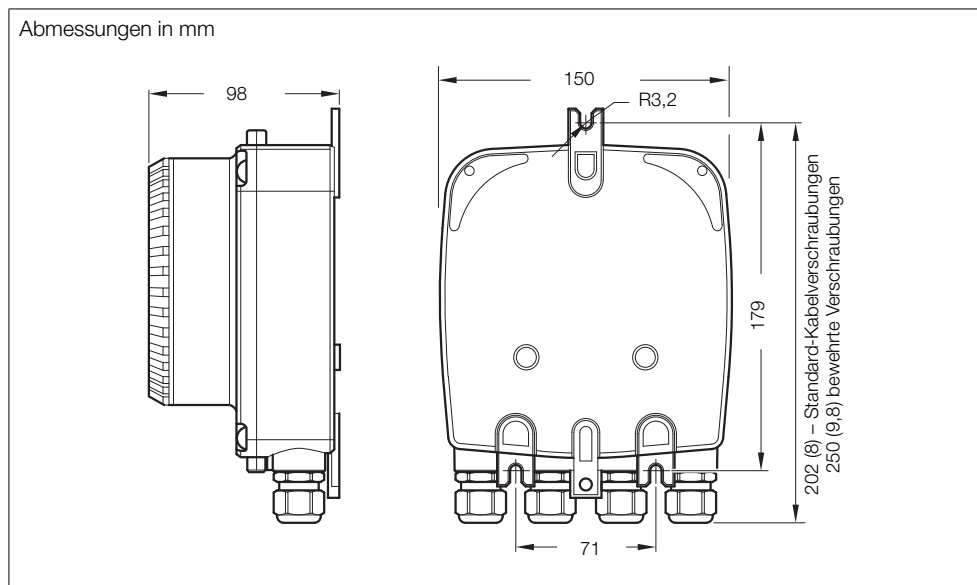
Abmessungen für externen Messumformer (Abbildung mit Standard-Kabelverschraubungen)
